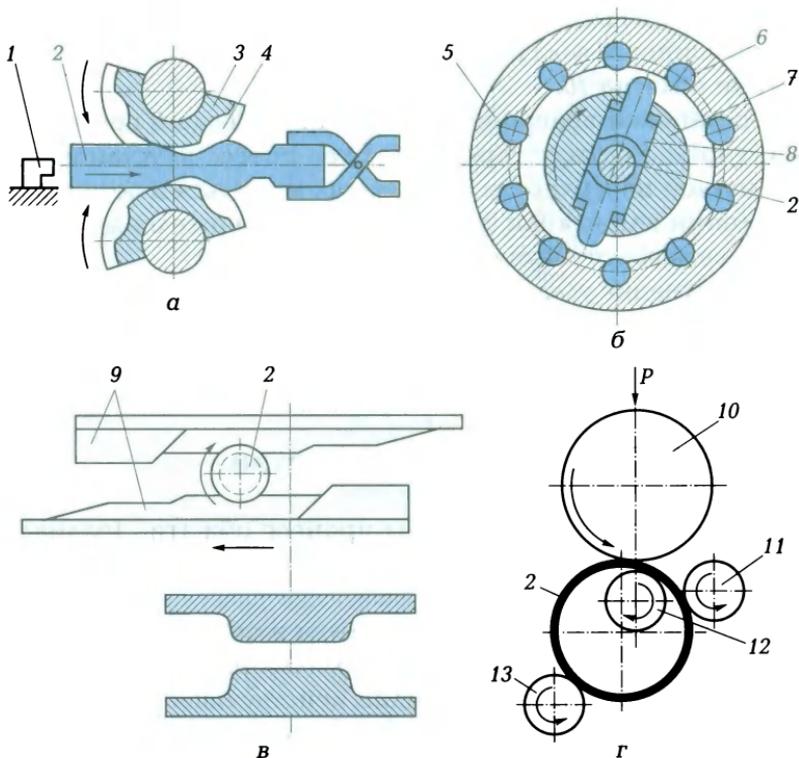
Схемы действия ковочных вальцов [а], ротационно-ковочной машины [б], станков поперечно-клиновой прокатки [в] и раскатки [г]:
